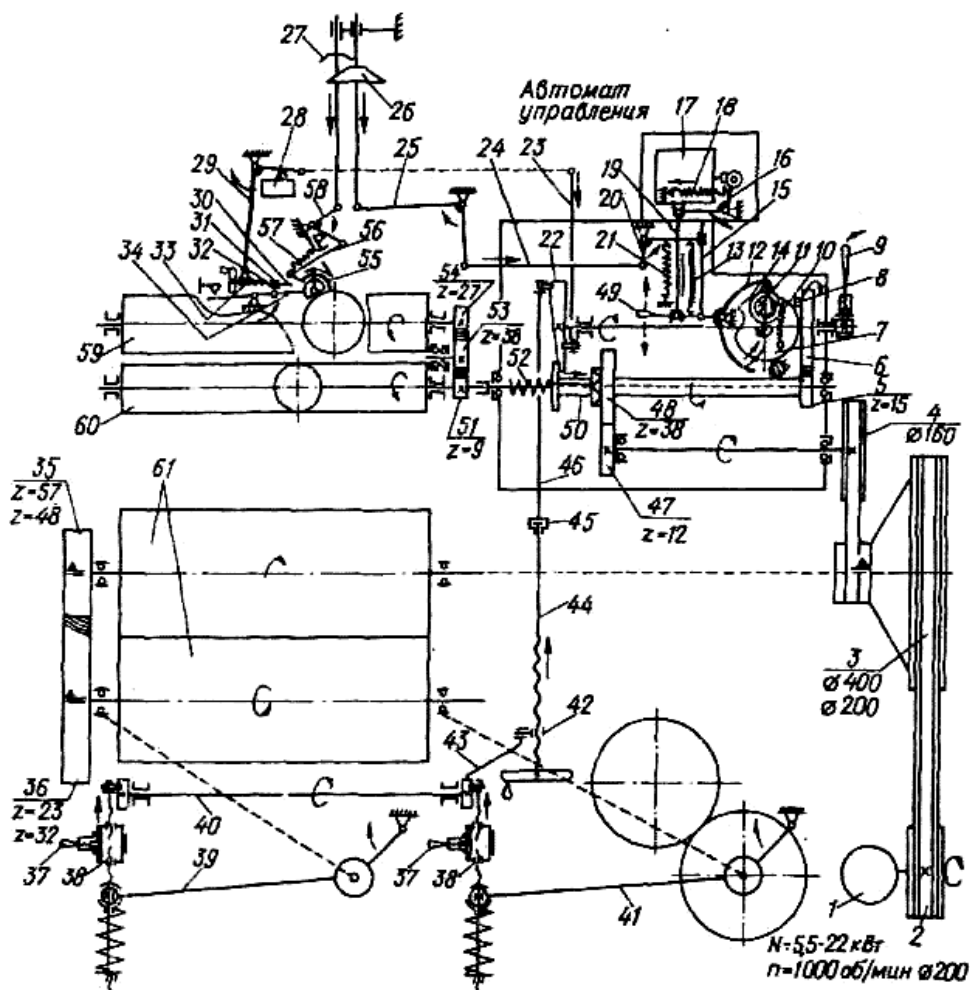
Кинематическая схема вальцового станка ЗМ2: 1- электродвигатель; 2, 3, 4- шкивы; 5, 6, 47, 48- зубчатые колеса автомата управления; 7 - диск; 8 - упор; 9 - руко-
